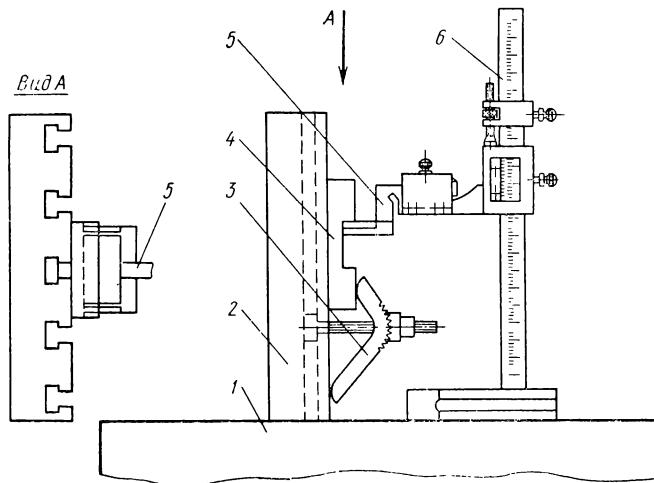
Схема закрепления детали в приспособлении, смонтированном из элементов УСП
